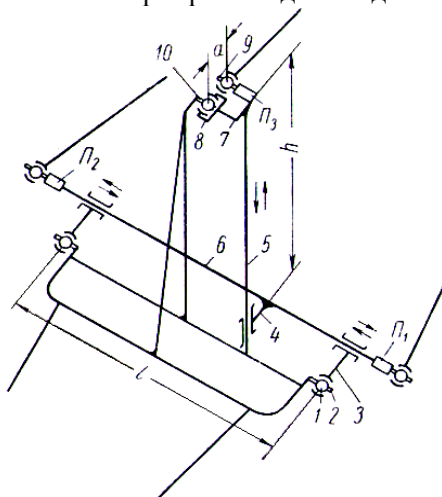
Схема динамометрической рамы НАТИ: 1-сферический шарнир; 2-тензометрический палец; 3-нижний кронштейн; 4-кронштейн; 5-стойка; 6-горизонтальная ось; 7-вилка; 8-сферический шарнир; 9-тензометрический палец; 10-соединительный палец машины
